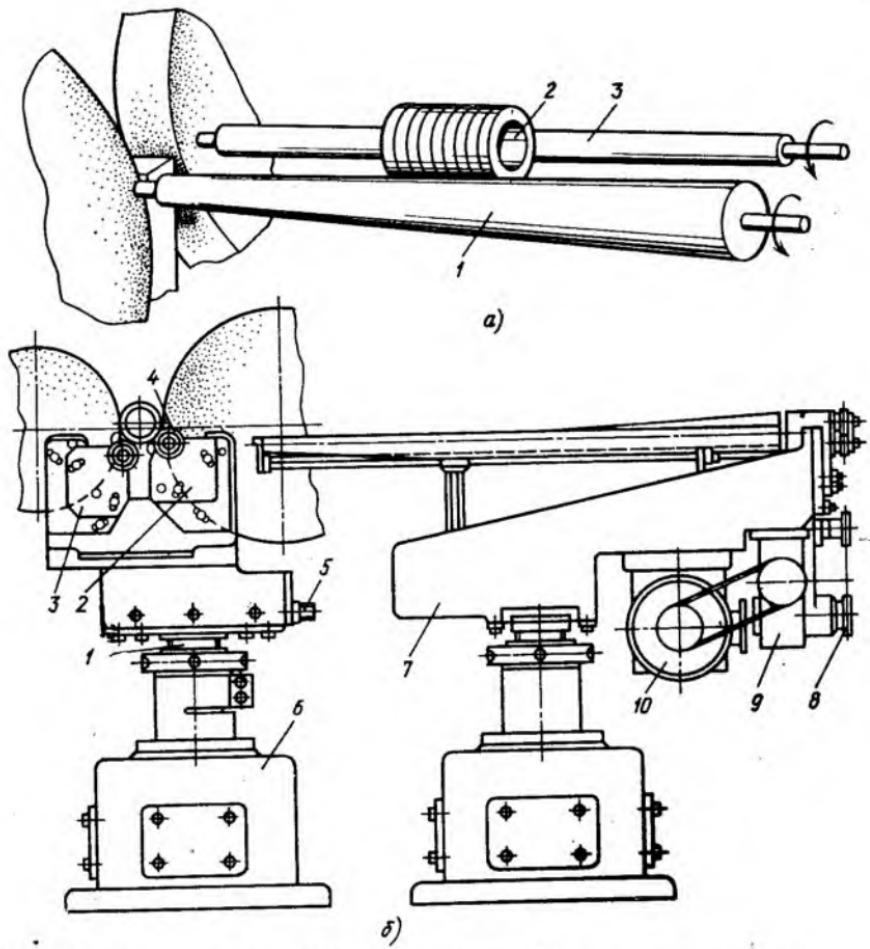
Принцип работы (а) и конструкция (б) двухвалкового загрузочного устройства
